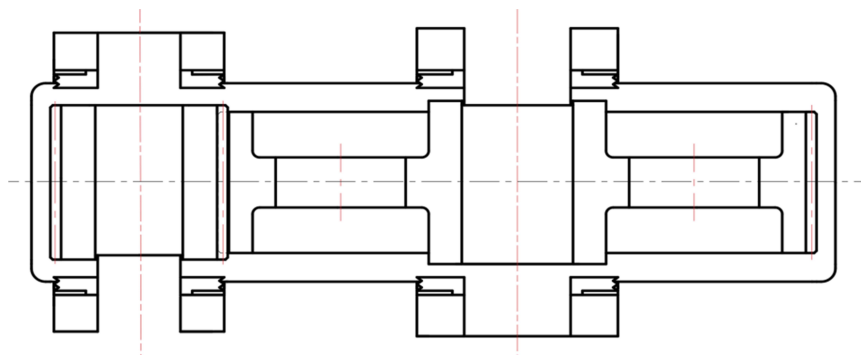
Изображение в редукторе опор с мазедерживающими кольцами
